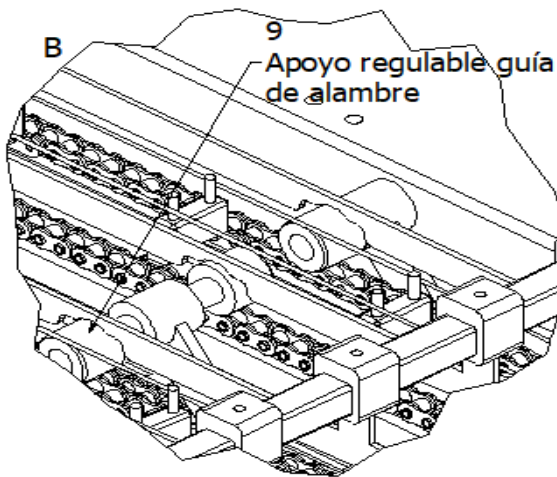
DETALLE APOYO DE GUÍAS
